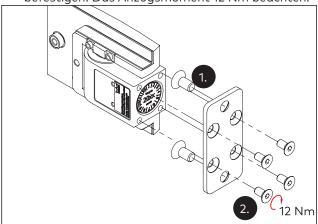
Befestigung der Montageplatten am Pendeltürband
